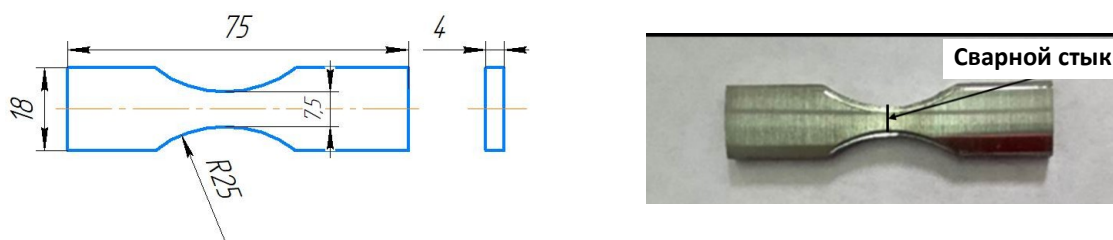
Образец со сварным соединением для испытаний на усталость
